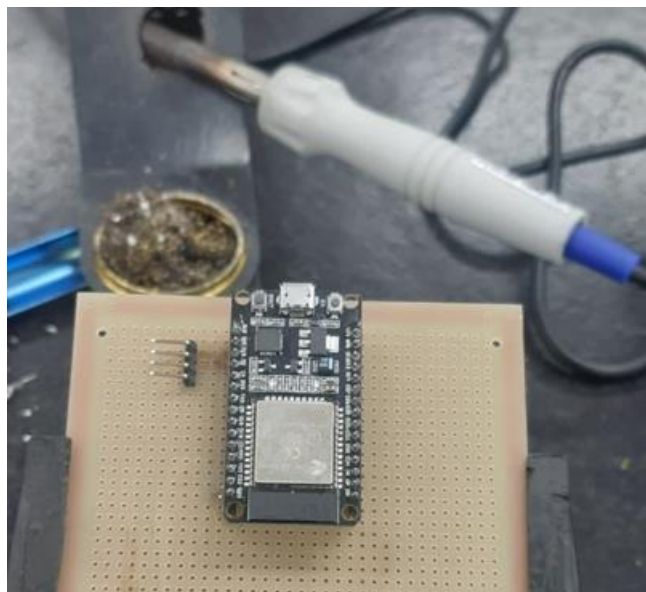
Soldagem dos terminais e borne na placa ilhada, observa-se o diodo de proteção de sobre tensão.
